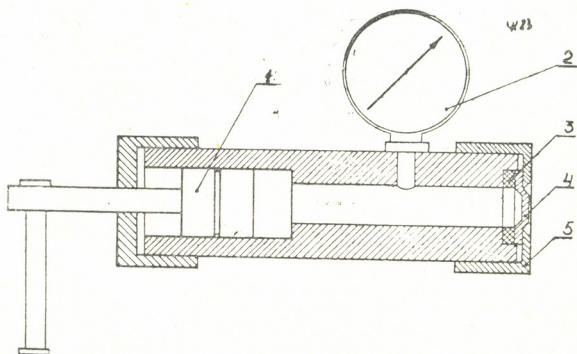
Схема установки для испытания на герметичность: 1) плунжер, 2) манометр, 3) прокладка, 4) образец, 5) крышка
